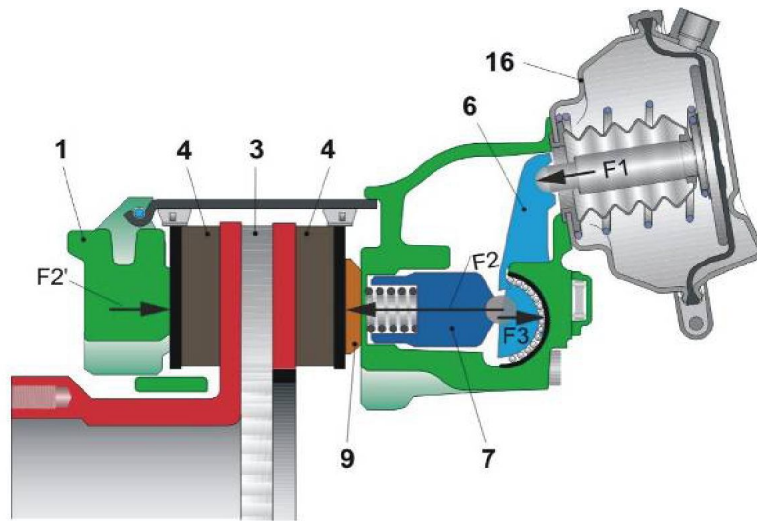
Схема роботи дискового гальмівного механізму:
